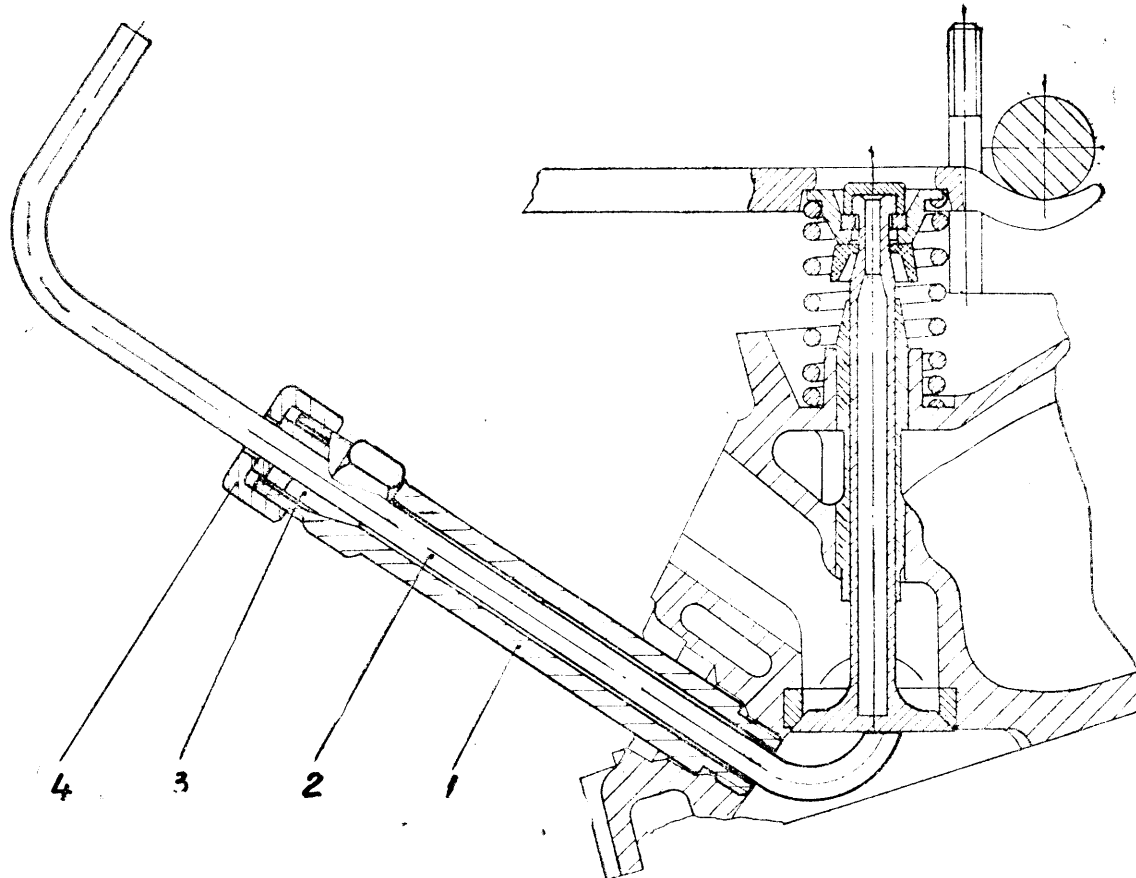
Auswechseln der Ventildeder ohne Ausbau des Zylinderkopfes, mit Hilfe der Vorrichtung M-8
